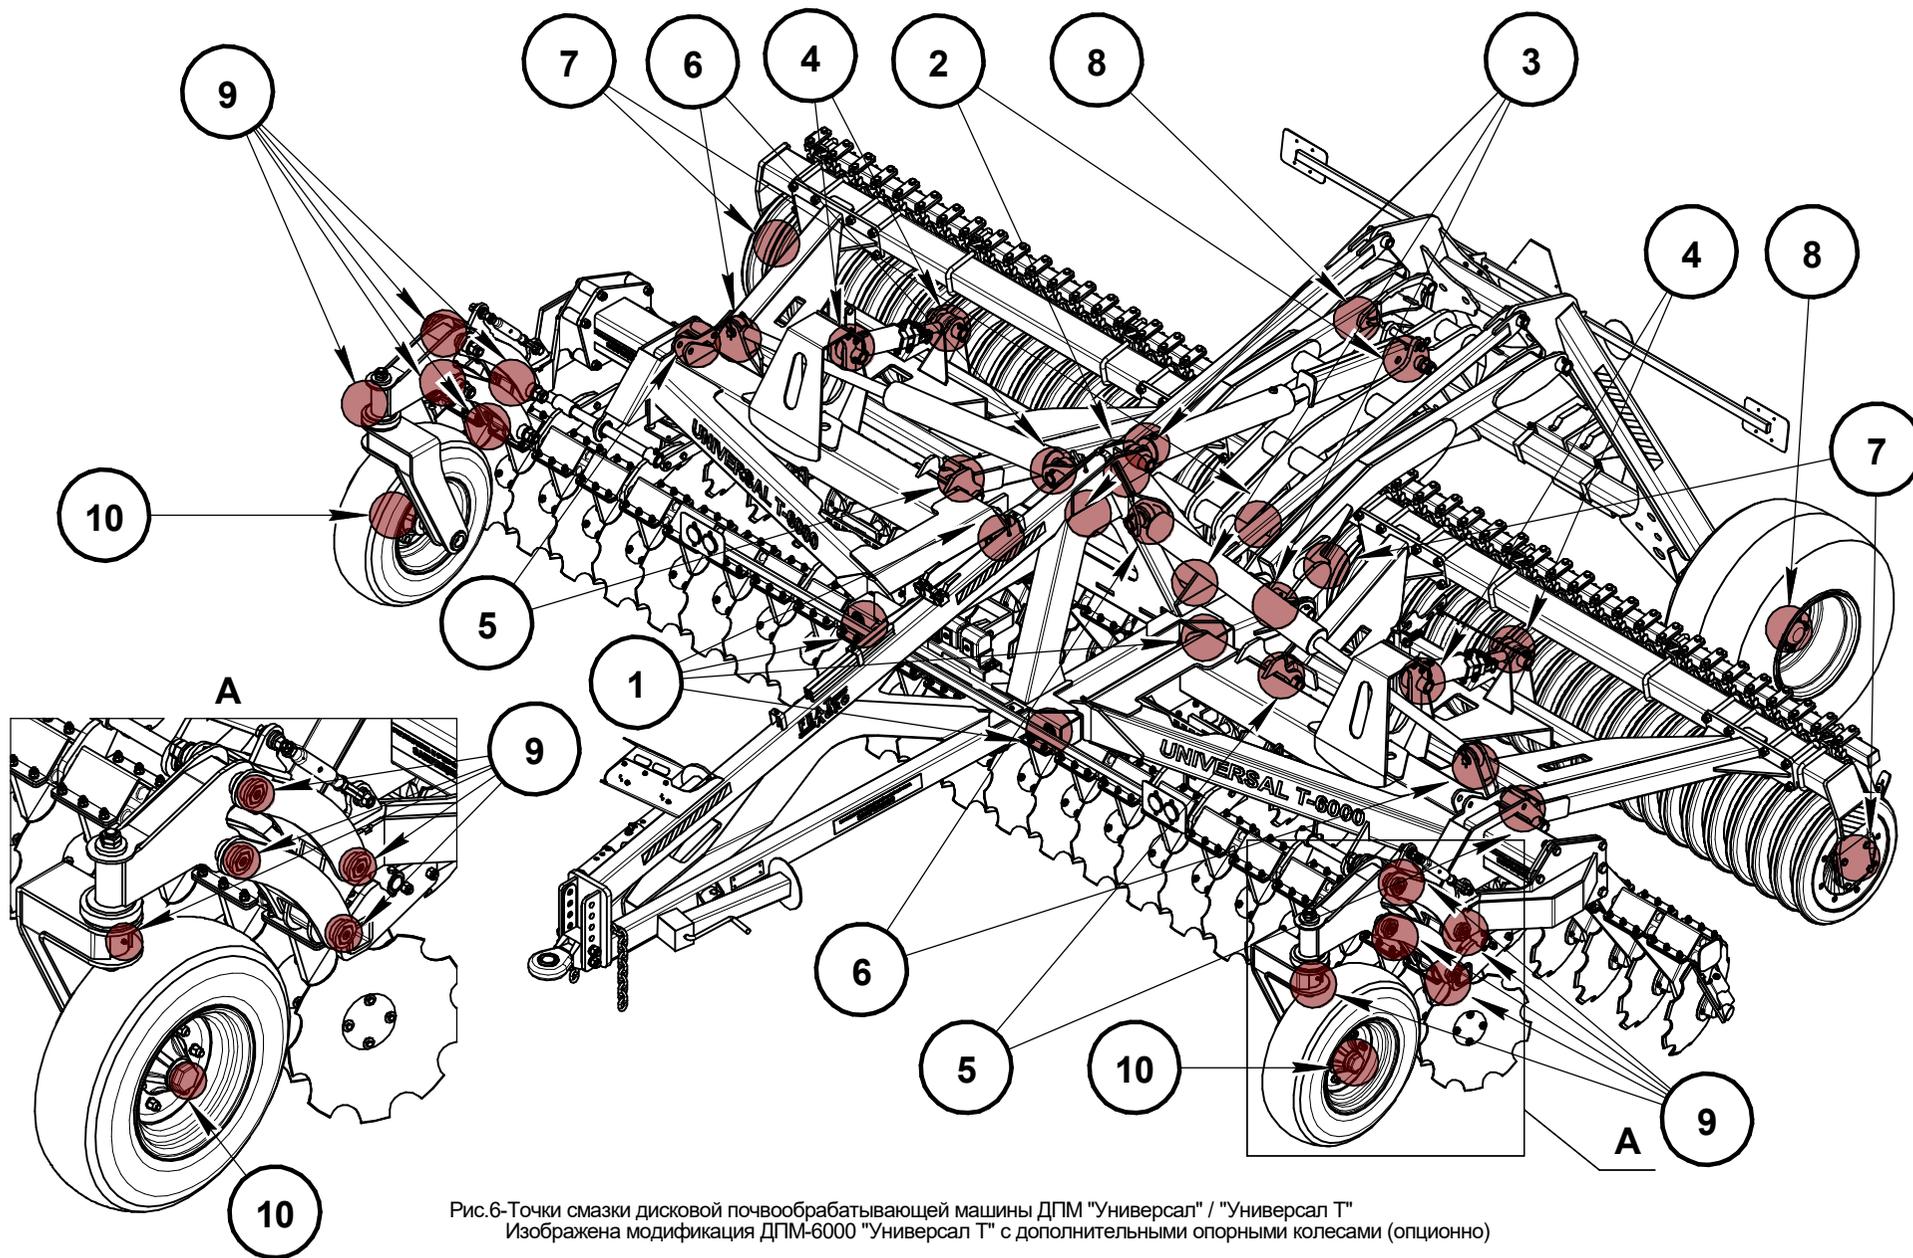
Точки смазки дисковой почвообрабатывающей машины ДПМ "Универсал" / "Универсал Т"
